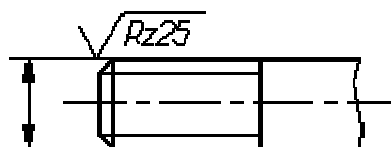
Пример обозначения шероховатости наружной резьбы
